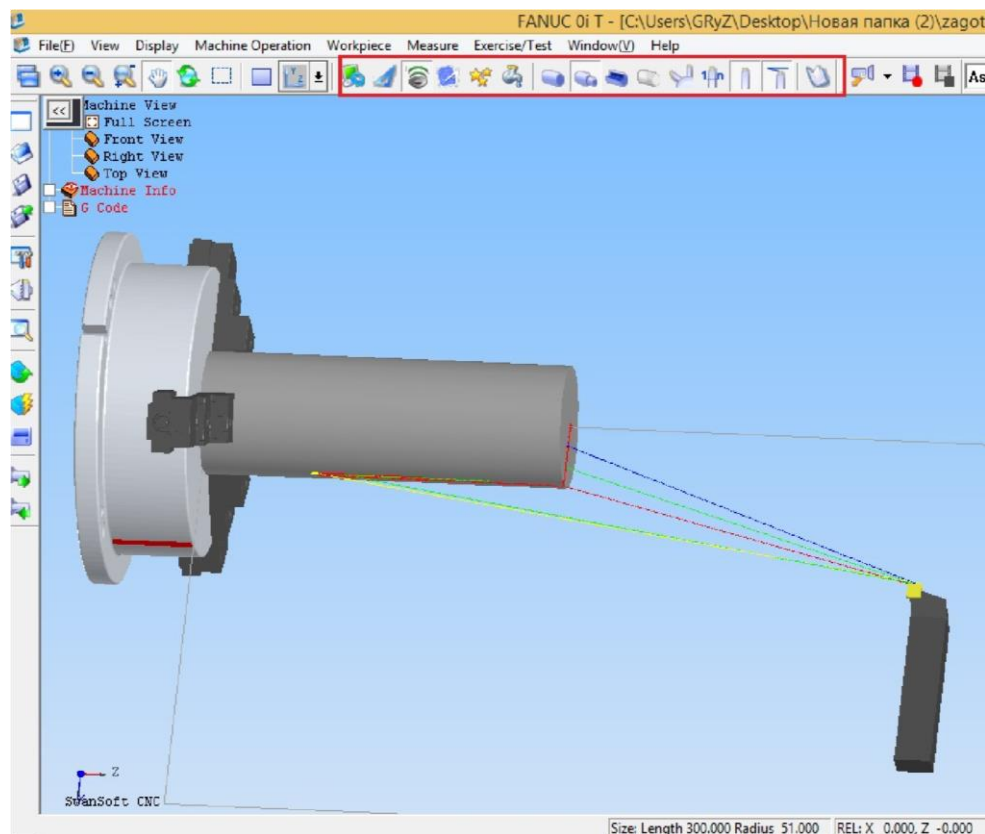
Комфортний вигляд перегляду обробки деталі
